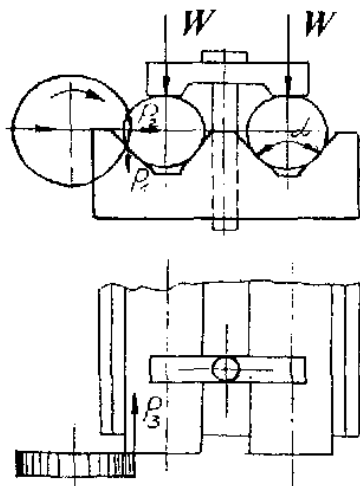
Затиск заготовки прихватами на призмах при фрезеруванні
